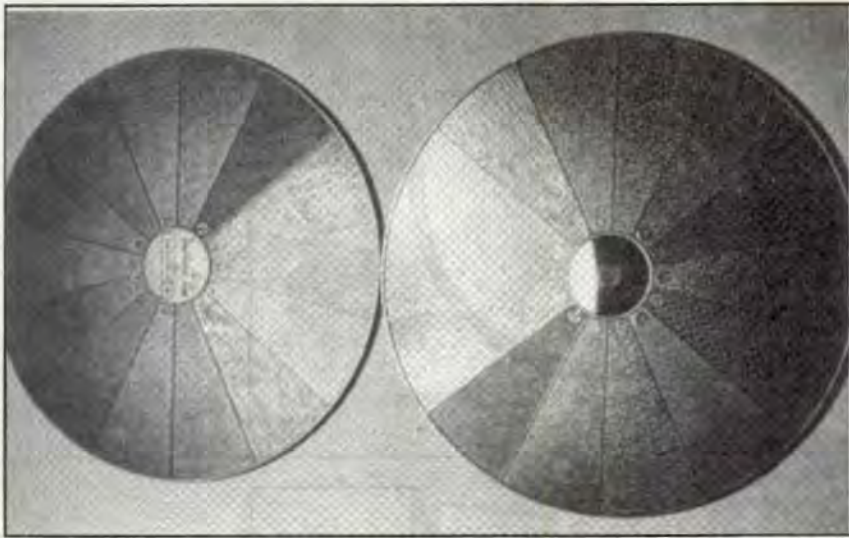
Estructuras fotograbadas: a la izquierda, una placa mate de ABS, a la derecha una placa brillante de PVC
